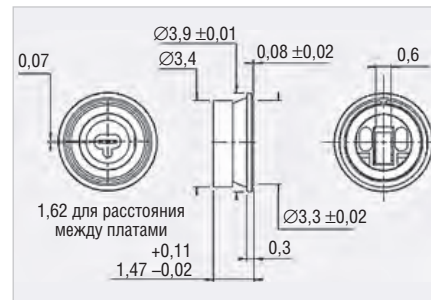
Конструкция соединителя IMP-LP типа R107802000
